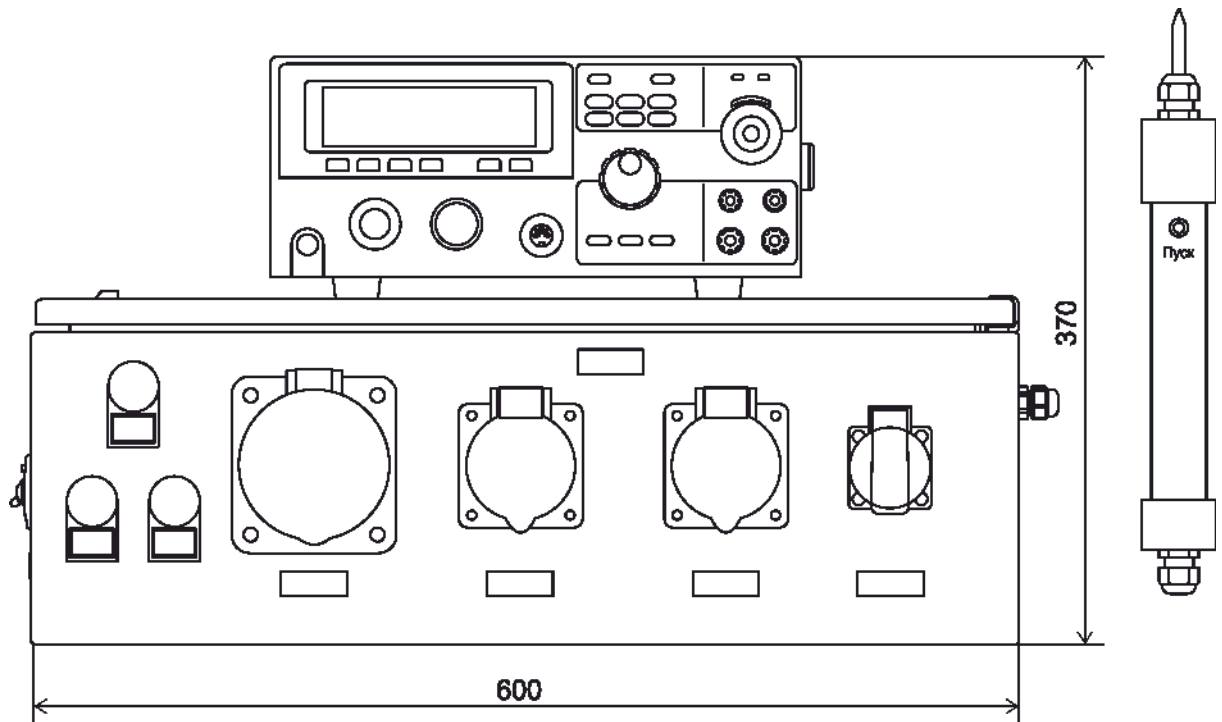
Габаритные размеры шкафа СЭБ-2
